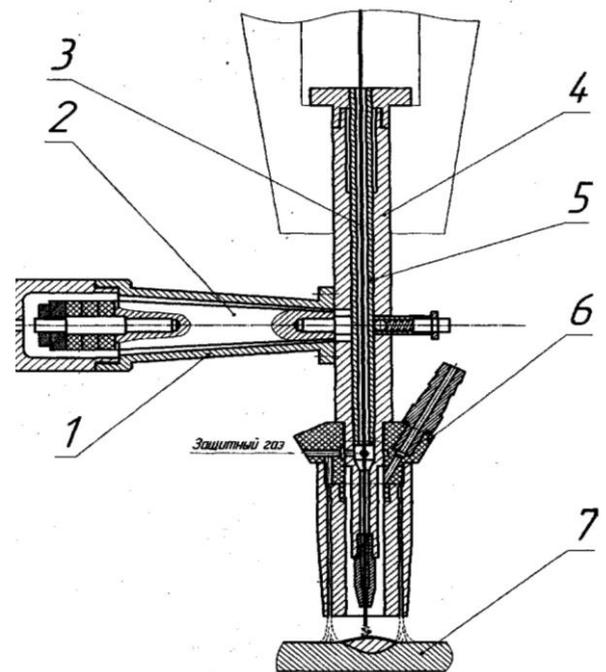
Схема технологической оснастки для введения ультразвуковых колебаний и порошкового материала в зону наплавки: 1 – устройство передачи УЗК на электрод; 2 – волновод-концентратор; 3 – электродная проволока; 4 – корпус наплавочной головки; 5 – токовод; 6 – устройство для подачи газопорошковой смеси; 7 – наплаваемая поверхность
